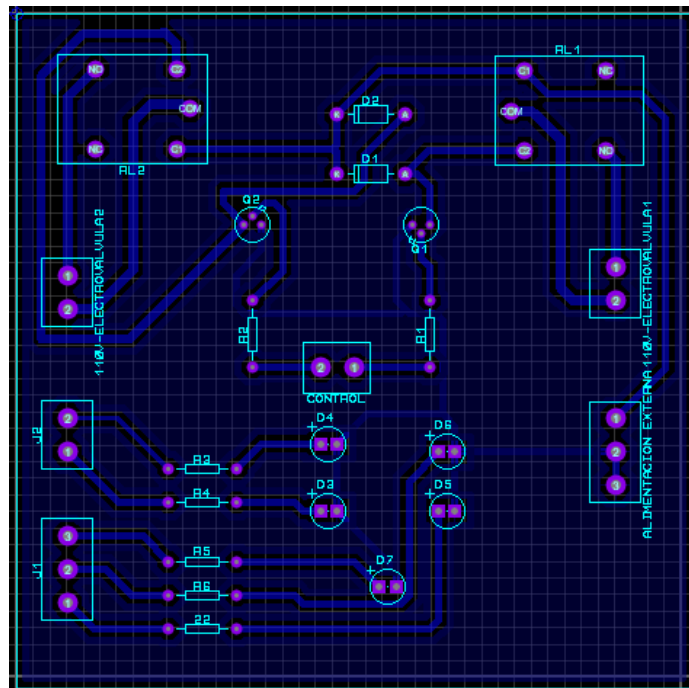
Diseño de PCB para el sistema de control. [Autor]
